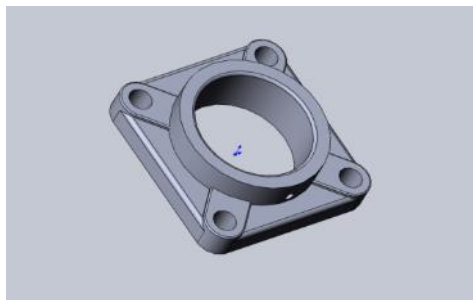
Корпус фланцевого підшипникового вузла UCF 208
